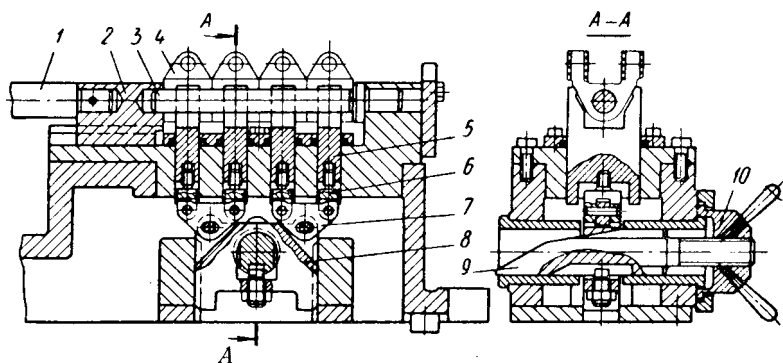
Многоместное фрезерное приспособление со сменной оправкой
